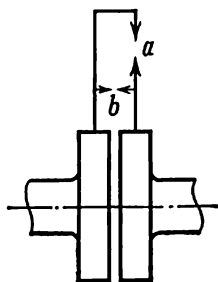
Installation des trusquins sur les plateaux du manchon d'accouplement
